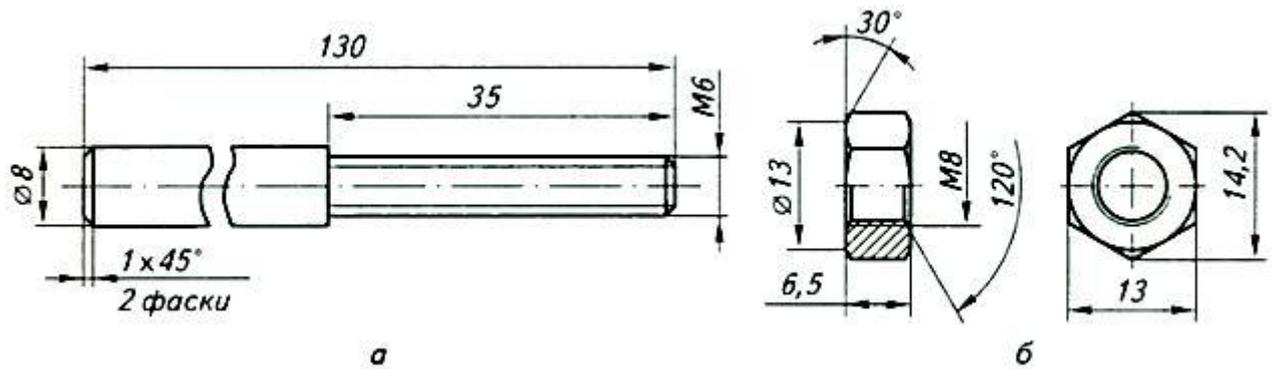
Чертежи деталей с резьбой, изготовленных на токарном (а) и фрезерном (б) станках: а — ручка воротка; б — гайка
